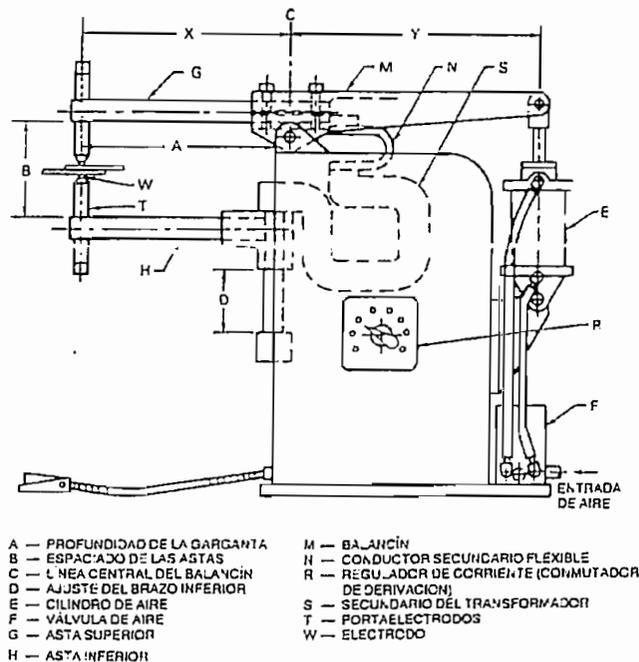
SOLDADORA TIPO BALANCIN
